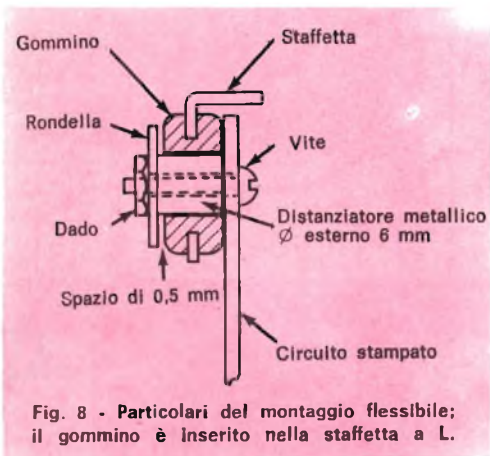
Particolari del montaggio flessibile; il gommino è inserito nella staffetta a L.
